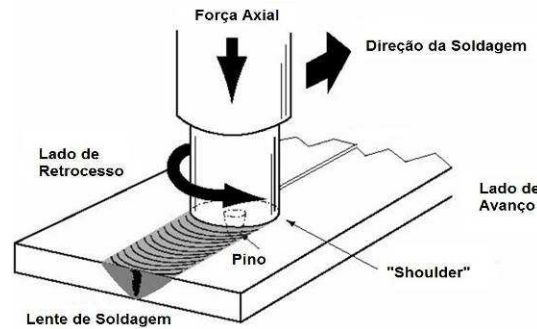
Esquemática do processo de *Friction Stir Welding*.<sup>(7)</sup>
